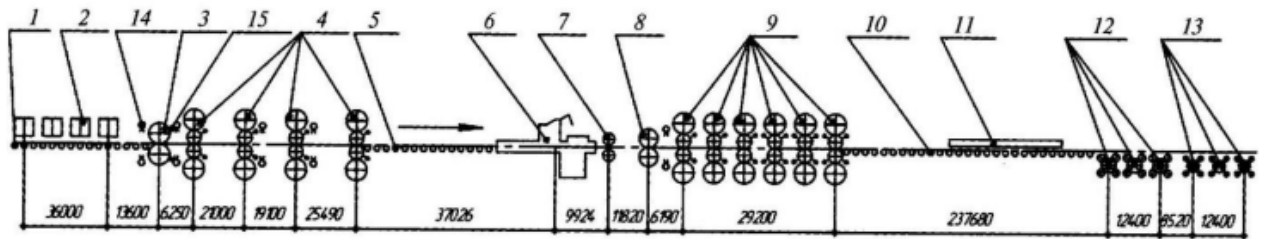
Схема розташування обладнання безперервного стану гарячої прокатки 1680 ПрАТ «Запоріжсталь»:
